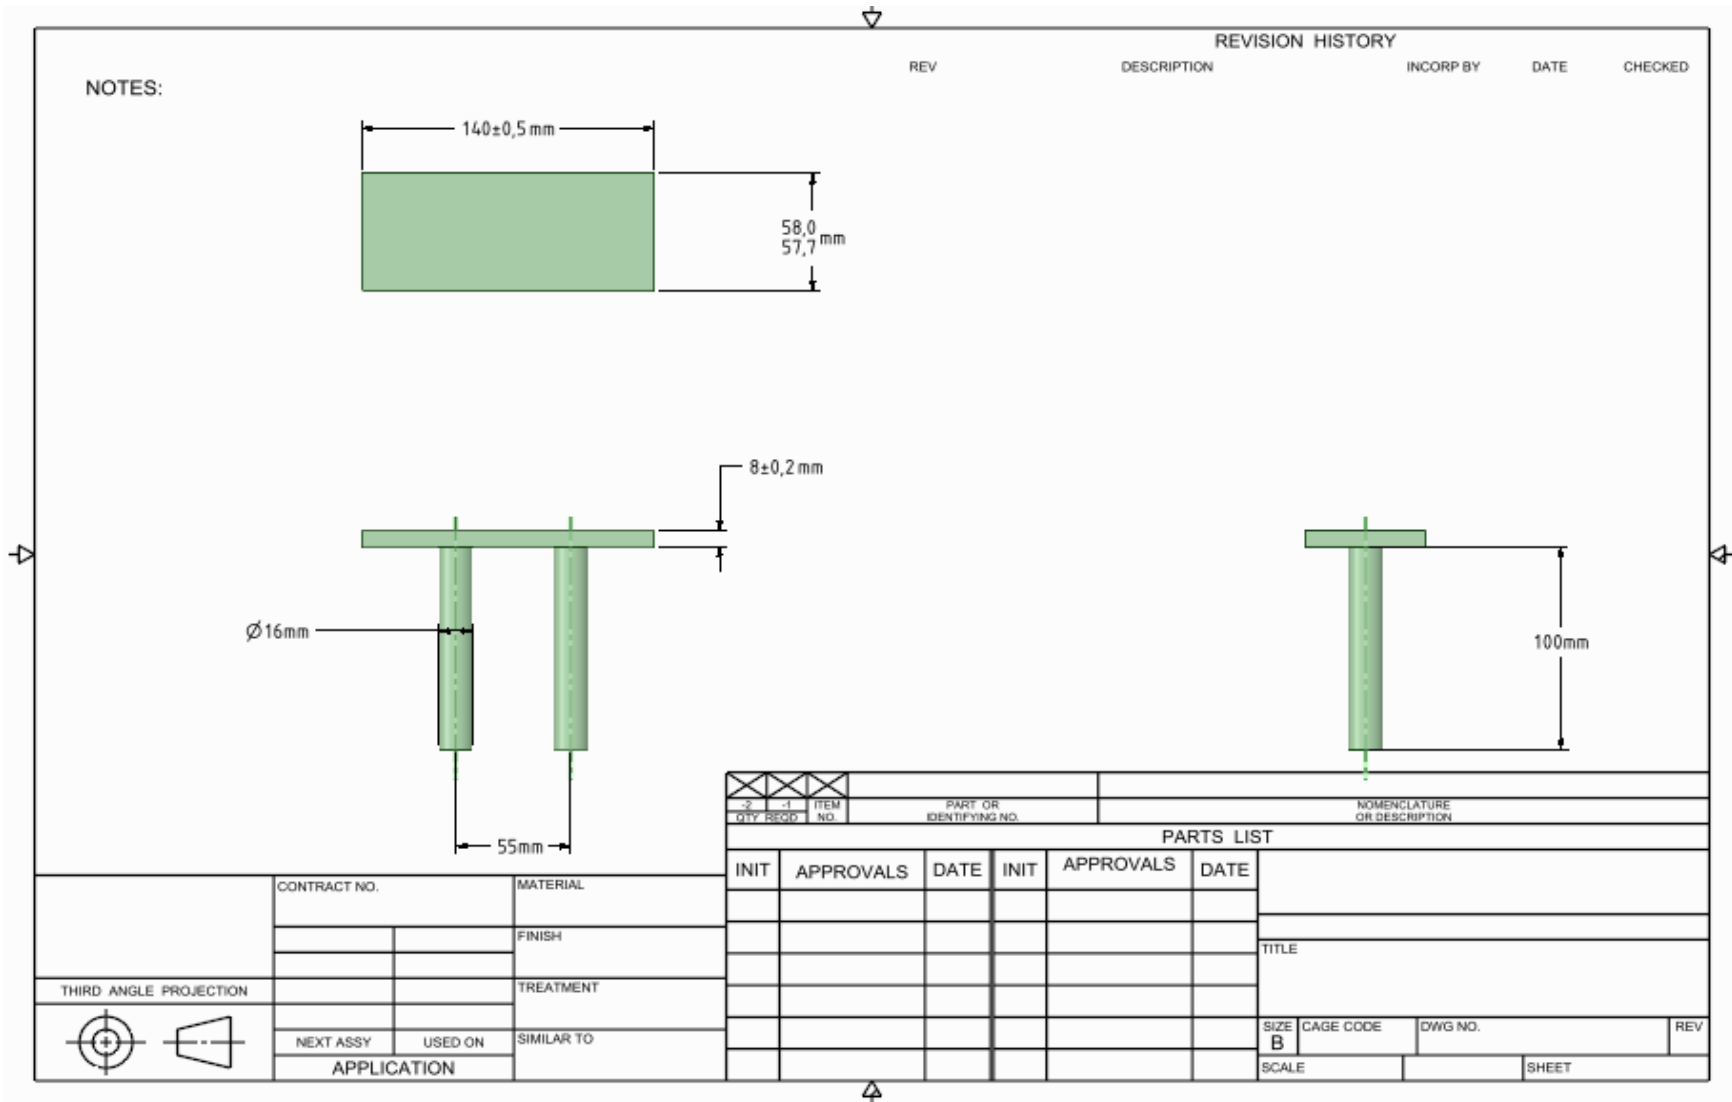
Planos de fabricación de la placa de apoyo para la contrapunta. Fuente: Elaboración propia.
